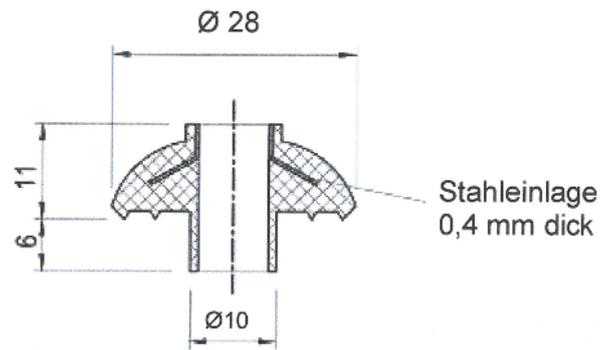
Pilzkopfdichtung aus Kunststoff mit Stahleinlage für die Sechskant-Holzschraube nach Bild 2.1 und für Stahlhaken nach Anlage 4, Bild 4.2
